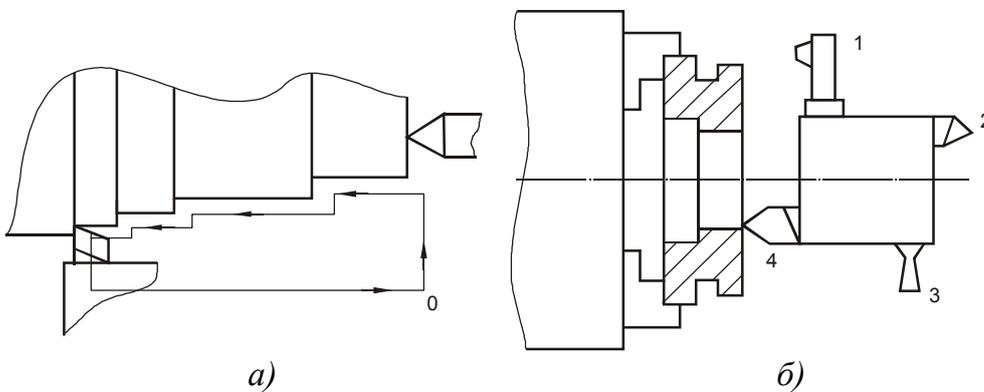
Одноместная последовательная обработка: а – одним; б – несколькими инструментами
